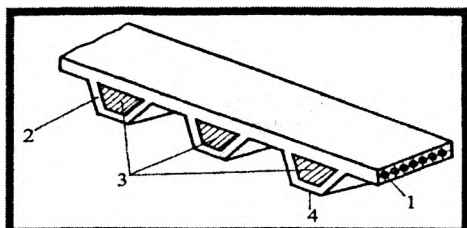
Зубчатый ремень с профильными вкладышами:
